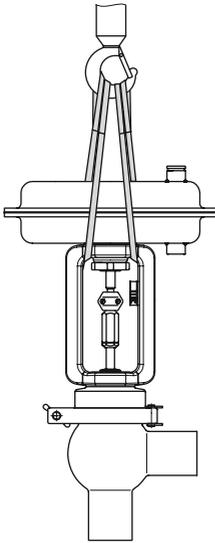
Typ 3347 mit Typ 3271 ohne Hebeöse
